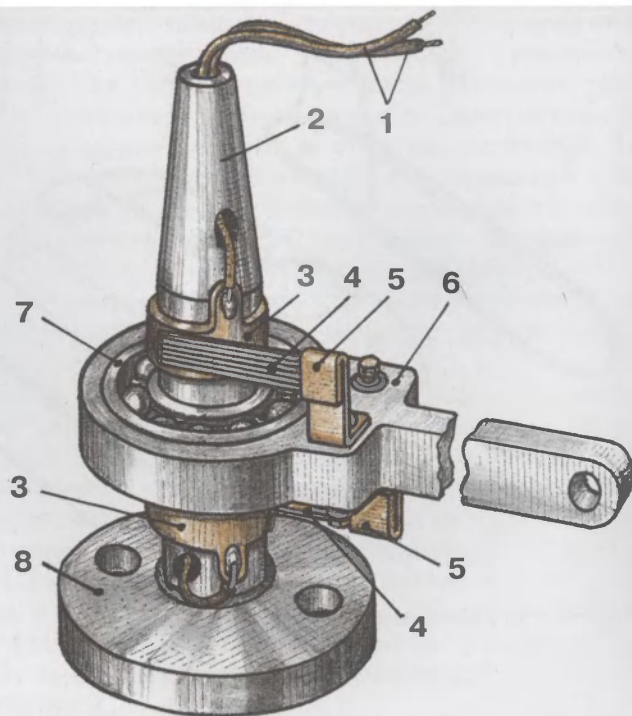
Общий вид центральной стойки корды: 1 — провода питания модели; 2 — корпус; 3 — токосъемное кольцо; 4 — щетка; 5 — хомут щетки; 6 — поворотная планка; 7 — шарикоподшипник; 8 — основание.
